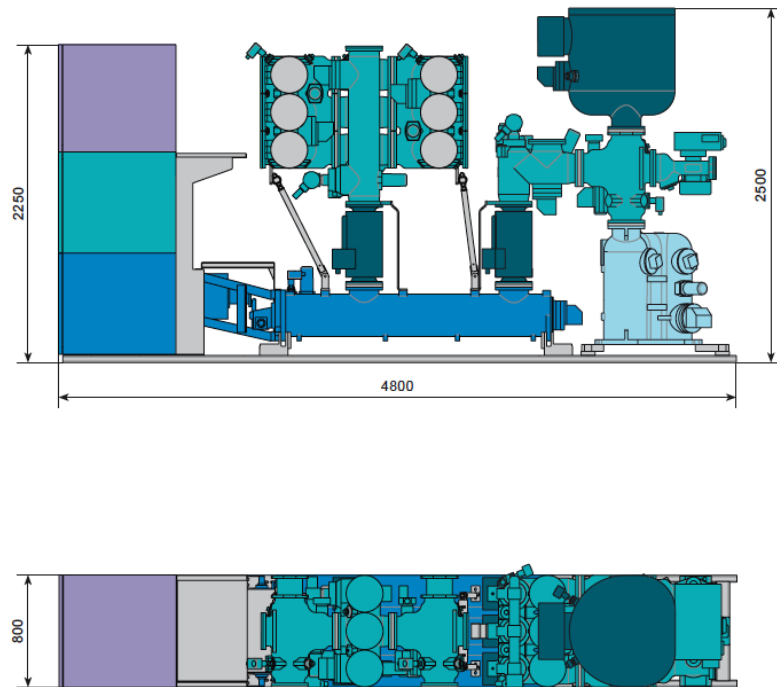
Alzado y planta del módulo GIS de 66 kV.
